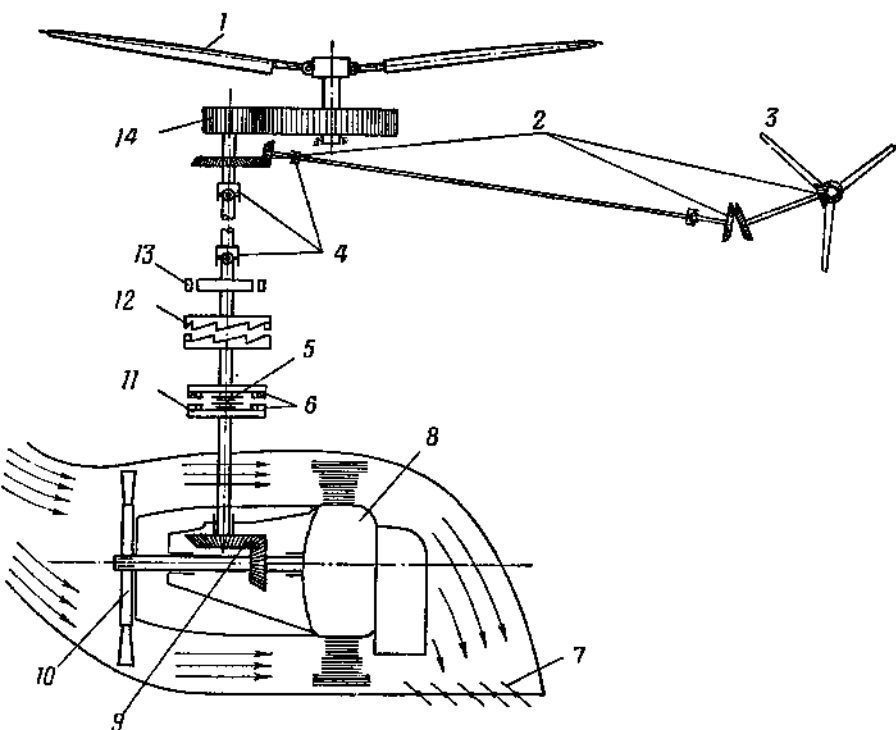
Схема силовой установки и трансмиссии одновинтового вертолета: 1 — несущий винт; 2 — редукторы угловой передачи; 3 — рулевой винт; 4 — универсальные шарниры; 5 — фрикционные диски; 6 — муфта включения; 7 — масляный бак; 8 — двигатель; 9 — редуктор угловой передачи; 10 — вентилятор; 11 — муфта включения; 12 — муфта свободного хода; 13 — тормоз несущего винта; 14 — главный редуктор
